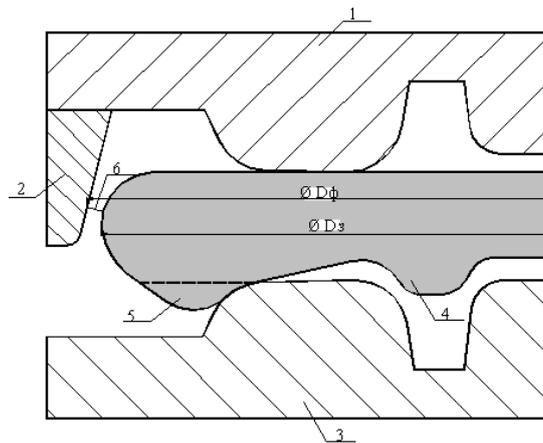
Первый момент штамповки колесной заготовки без гребня из осесимметричной осаженной и разогнанной заготовки:
